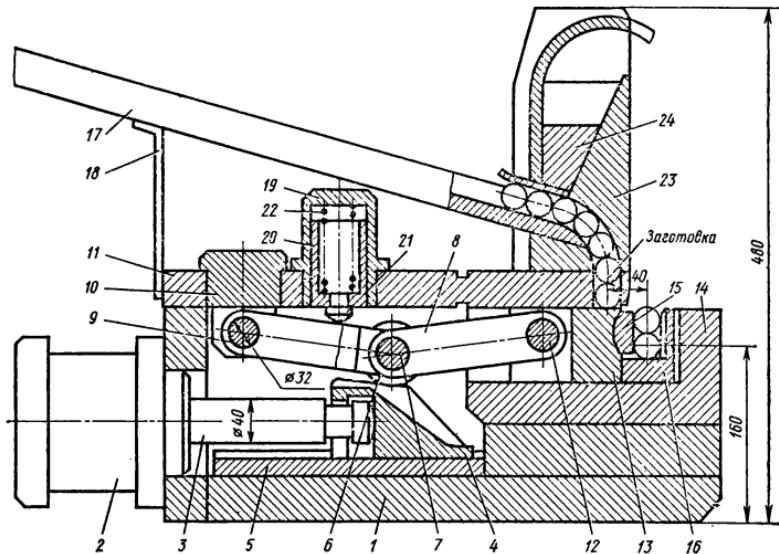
Приспособление для протягивания поверхностей пальцев рессоры
